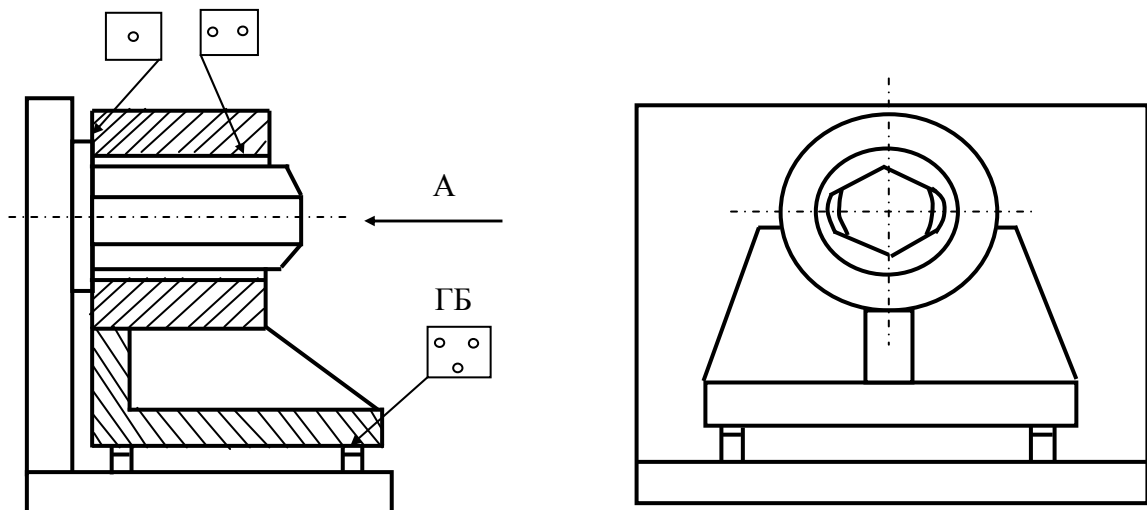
Базування деталей опори підшипника на опорах і пальцях
